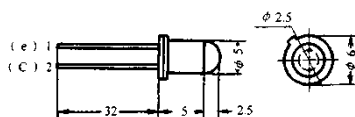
3DU11-33 型硅光电三极管外形结构尺寸图
